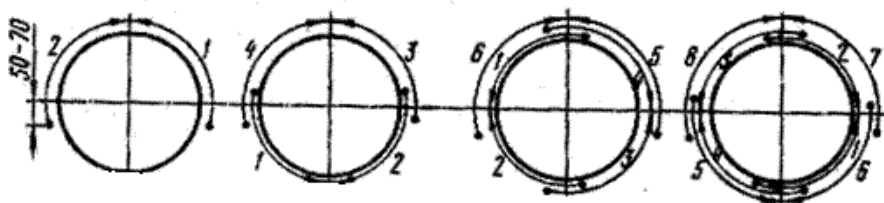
Схема сварки стыка трубы: а – второго слоя, б- третьего слоя
